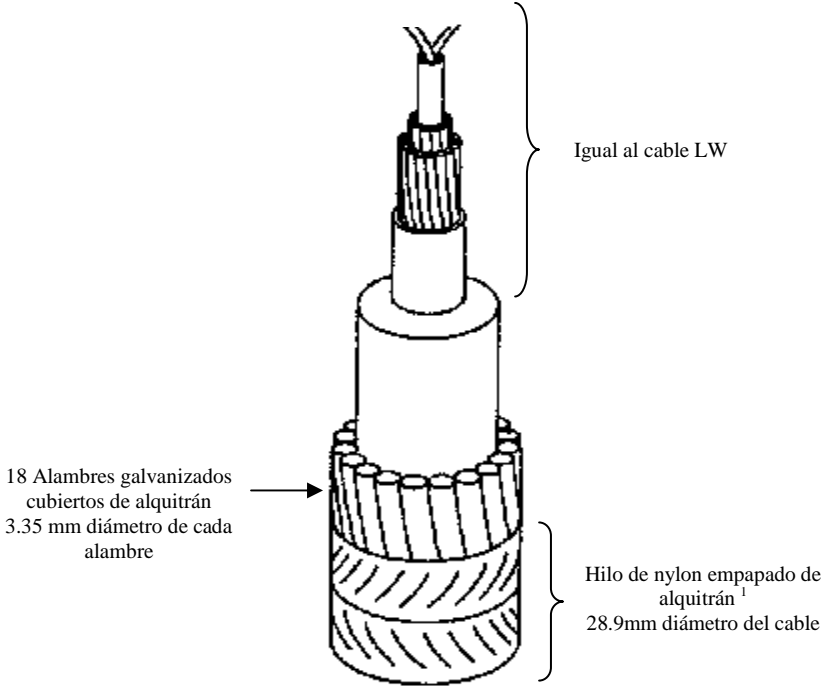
Cable SL 17 Armado con alambre Liviano (Light – Wire Armored Cable - LWA)
